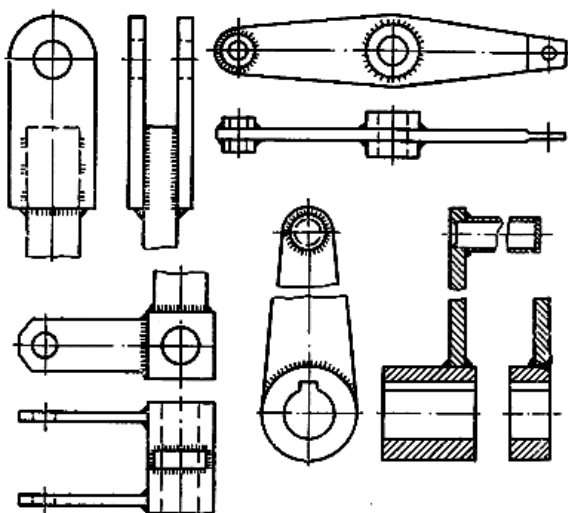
Типовые штамповарные заготовки зубчатых передач.
